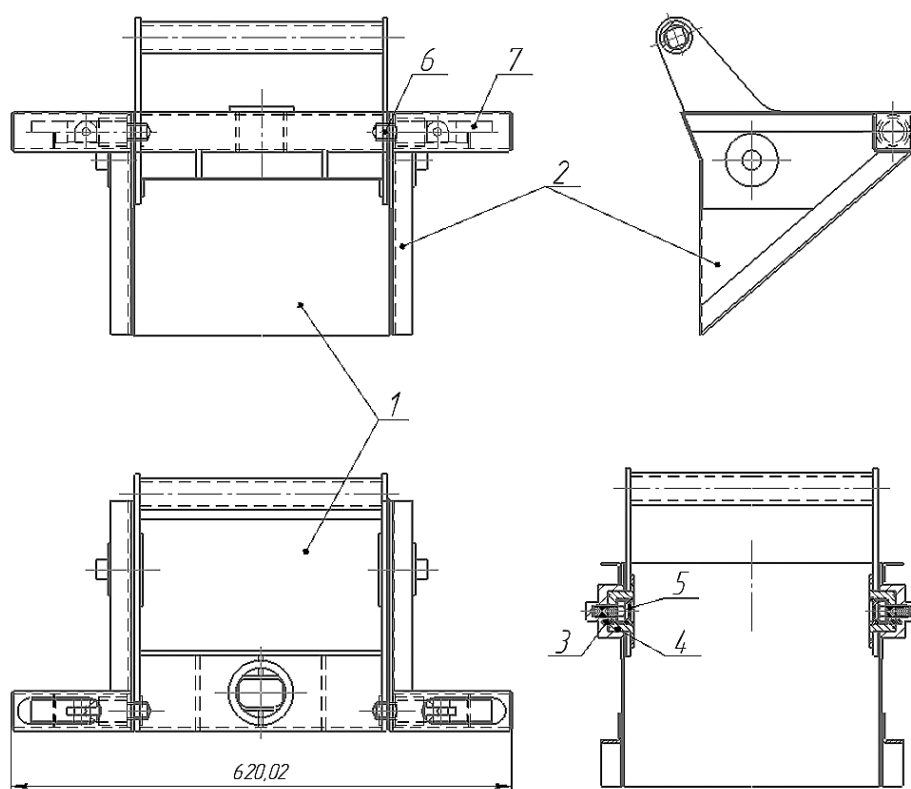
Стационарный счальный узел: 1 — кормысло; 2 — ниша; 3 — ось; 4 — крышка пальца; 5 — штифт; 6 — засов; 7 — ручка засова
